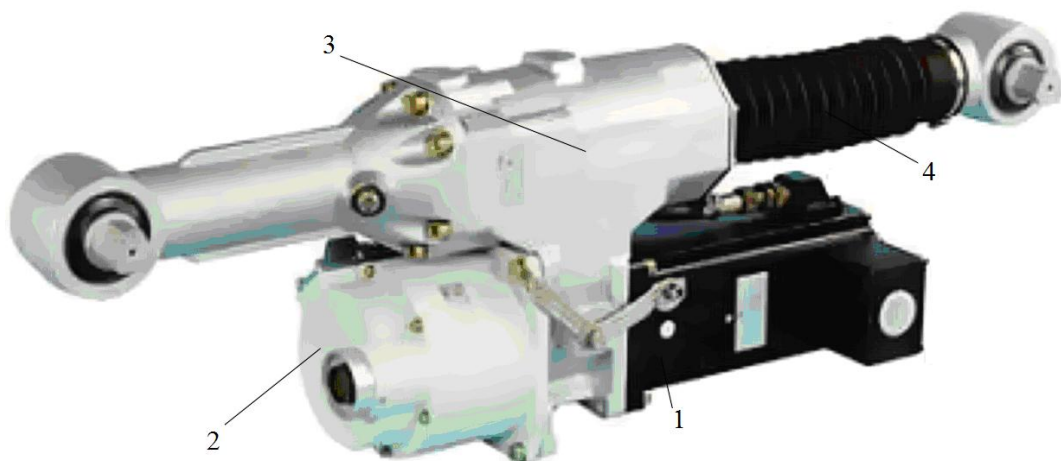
Електромеханічний привод для нахилу кузова вагона:
